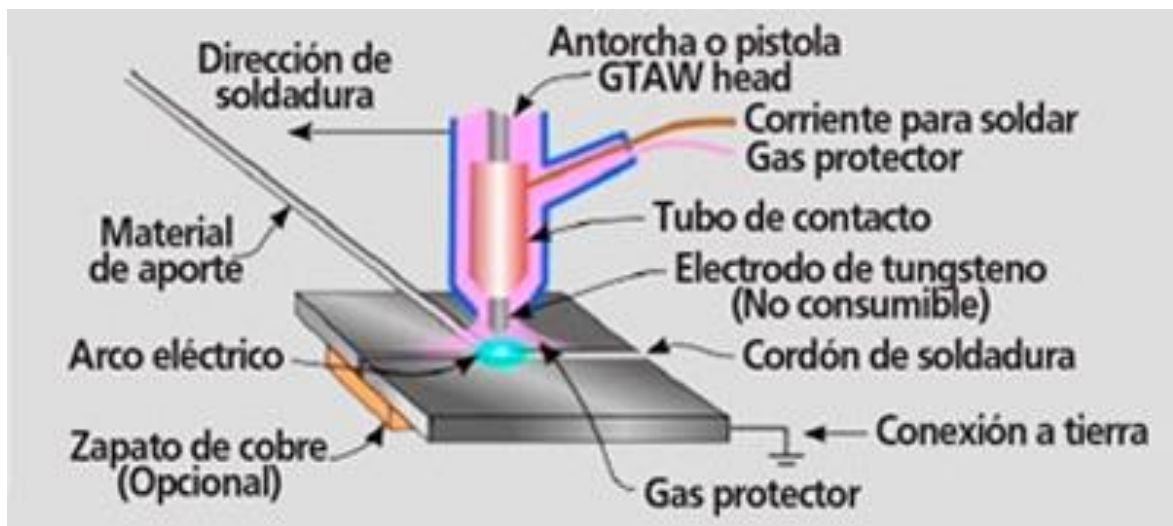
Esquema de la soldadura TIG (Font: ILMO)
